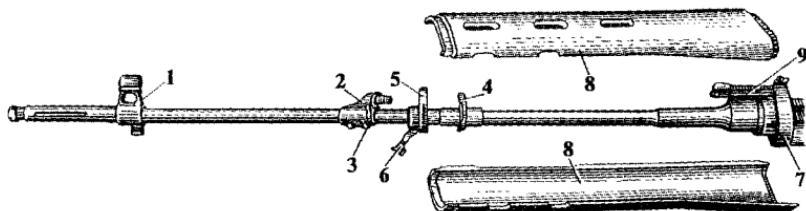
Ствол СВД-63: 1 — основание мушки; 2 — газовая камора; 3 — антабка; 4 — неподвижная часть верхнего упорного кольца; 5 — перемещающаяся часть верхнего упорного кольца; 6 — замыкатель верхнего упорного кольца; 7 — нижнее упорное кольцо; 8 — ствольные накладки; 9 — колодка прицела.
